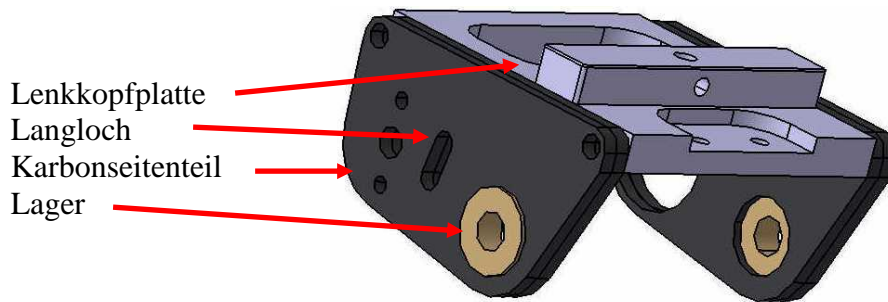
Frontantrieb Grundrahmen mit Lagern
